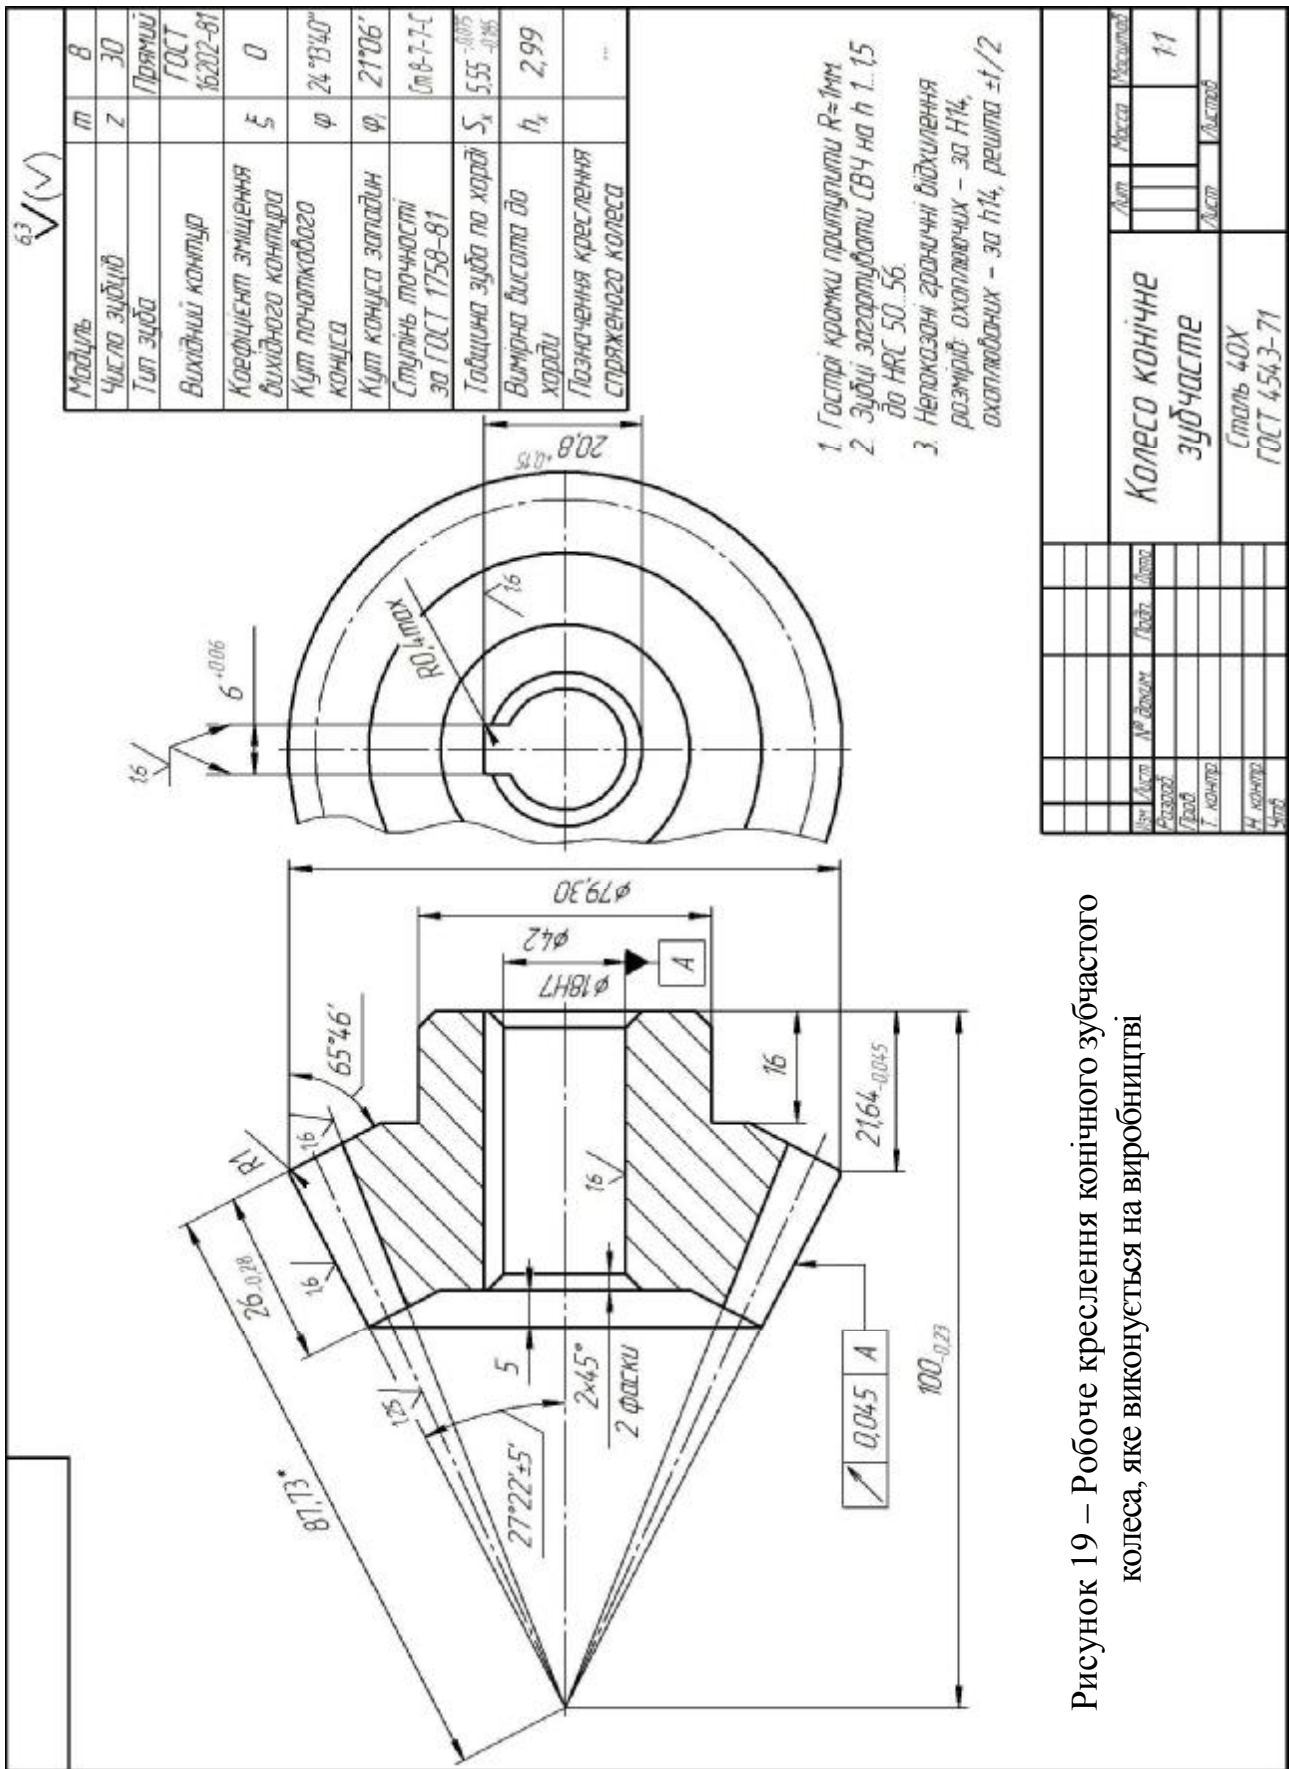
Робоче креслення кінцевого зубчастого колеса, яке виконується на виробництві
